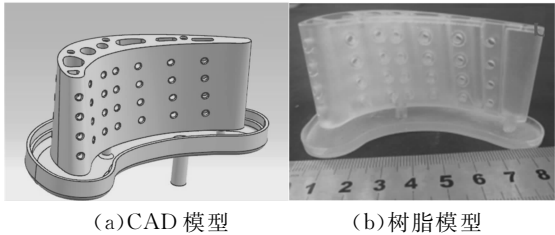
带冷却流道微孔叶片的局部 CAD 模型及其树脂模具
